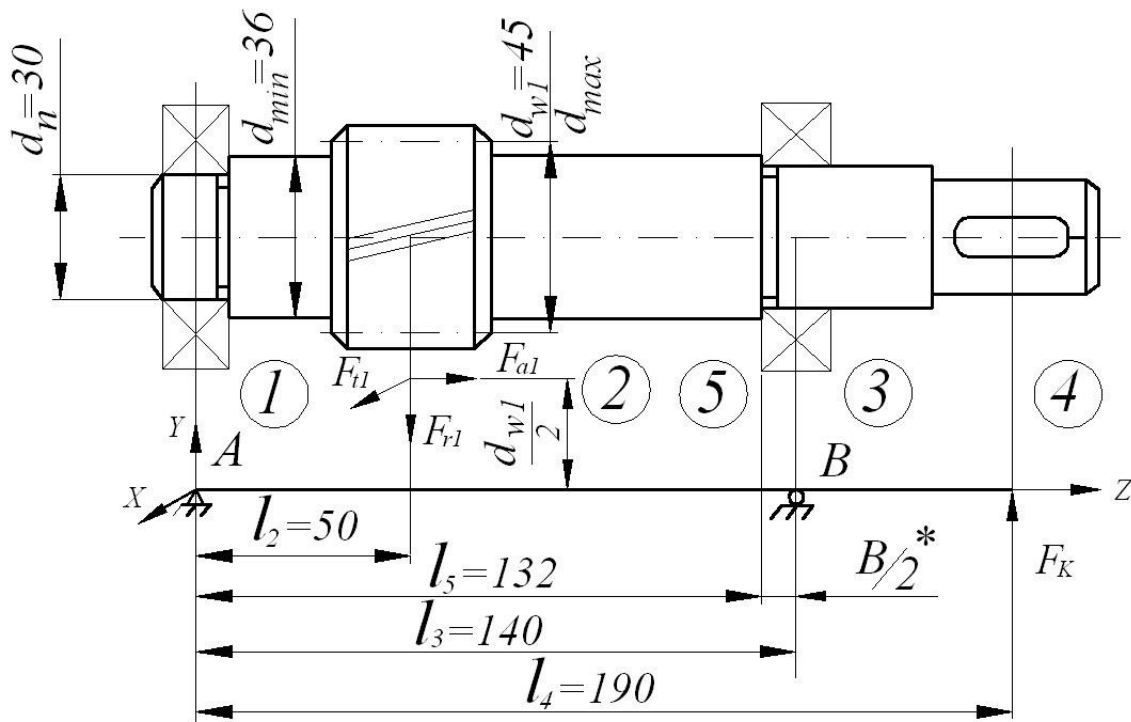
Схема быстроходного вала – шестерни: * – размер для справок (B – ширина подшипника для радиальных подшипников)
